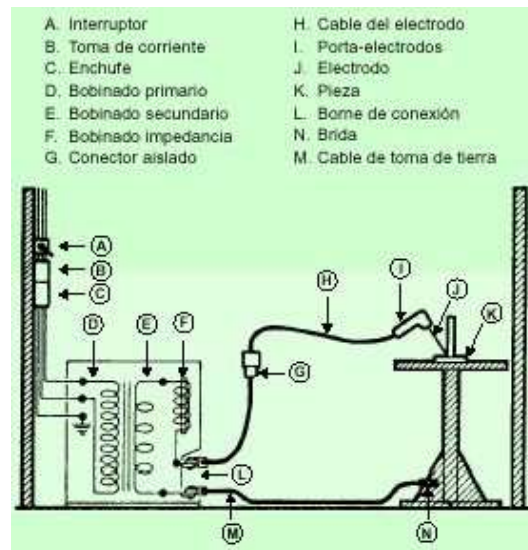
Instalación segura de un puesto de soldadura CA con transformador
